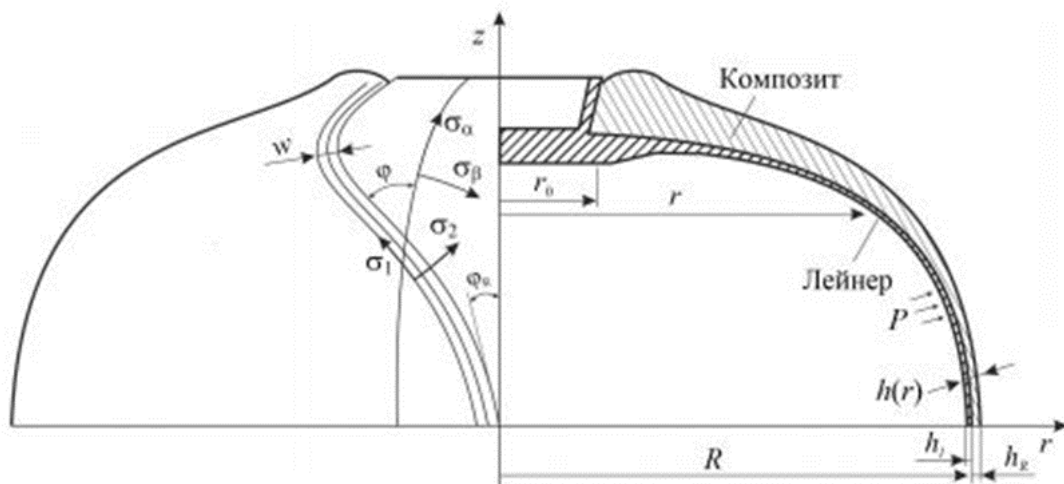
Конструктивна схема композитної конструкції
